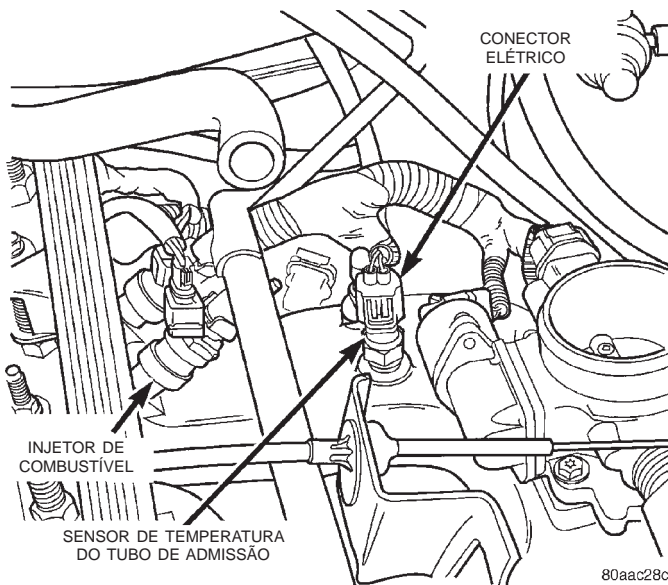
Localização do Sensor de IAT—Motor 2.5L
